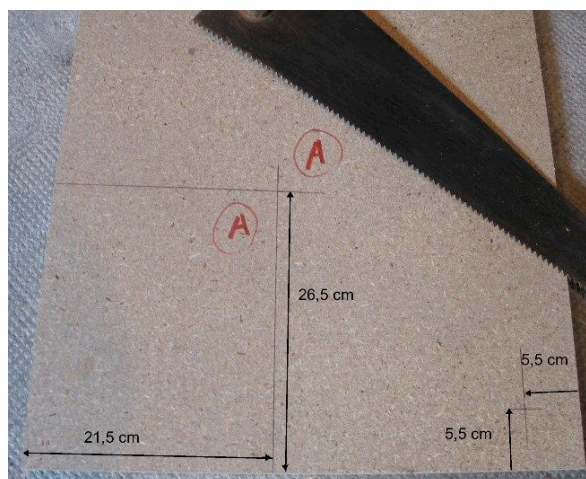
Tracé de la porte et de l'aération de façade (panneau A)
